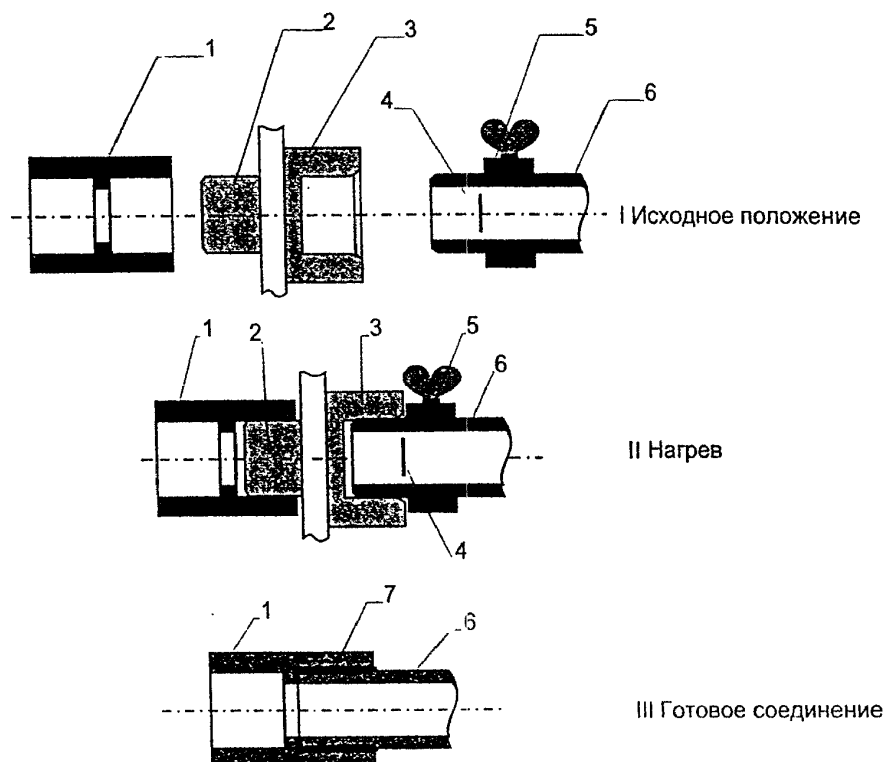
Последовательность процесса контактной сварки в раструб трубы и муфты из PPRC
